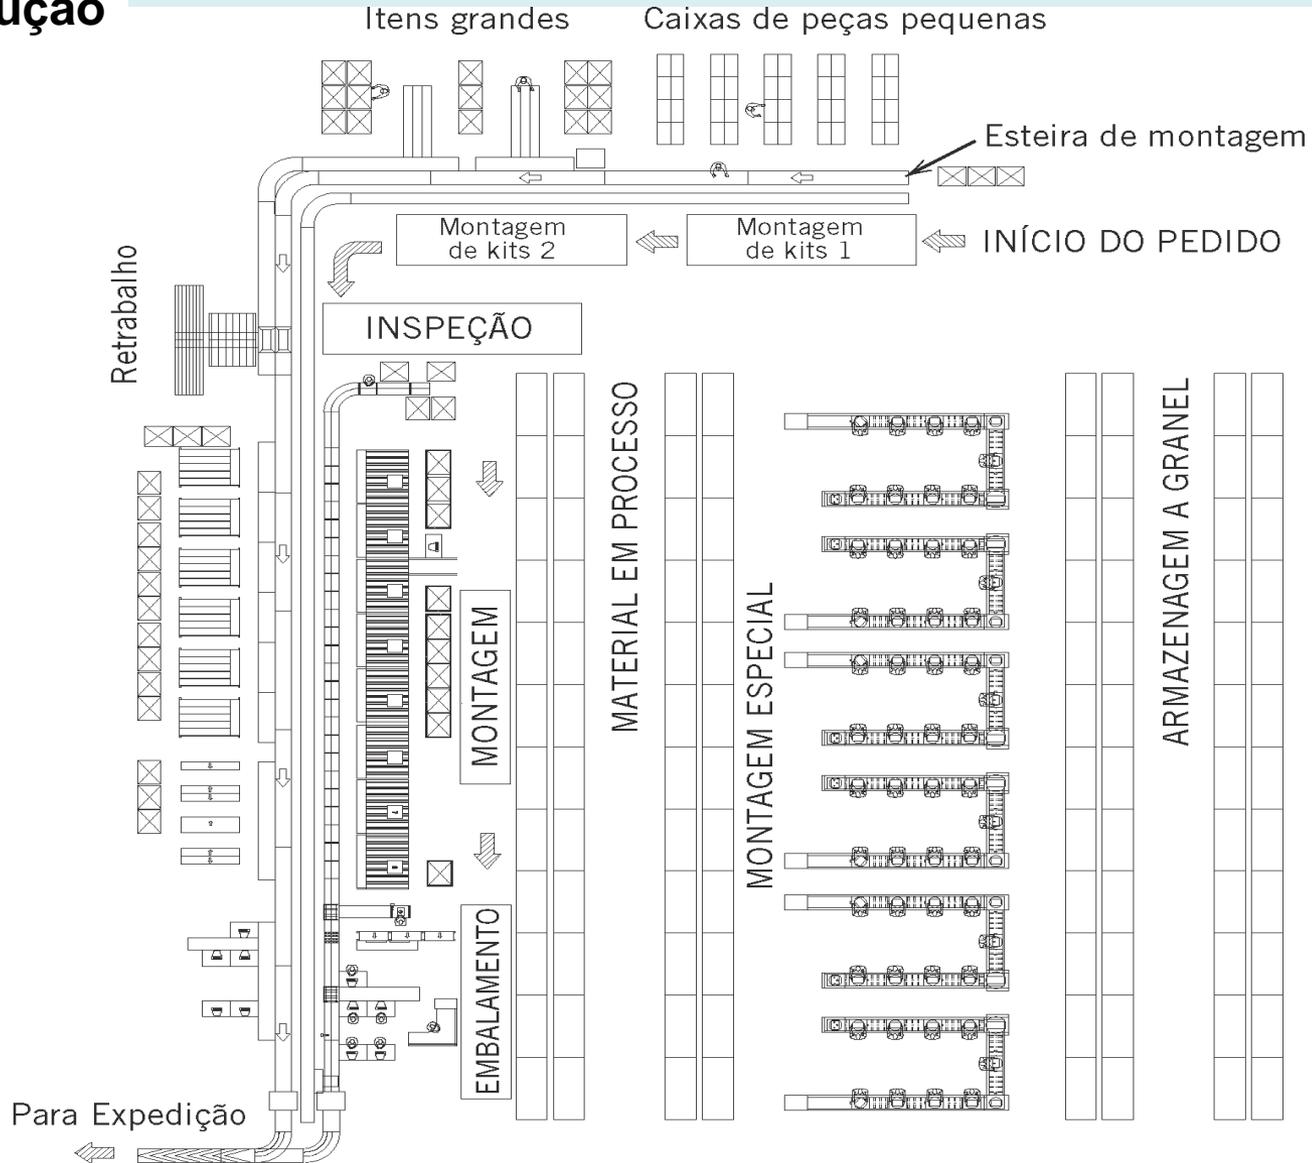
Arranjo físico 2-D de um departamento de montagem dentro de uma planta de produção. (Cortesia de Fortna Inc.)
